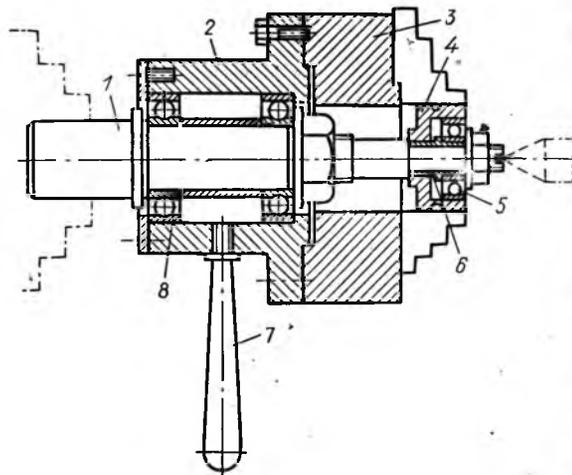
Приспособление для технологической приработки подшипников качения с твердым антифрикционным наполнителем
